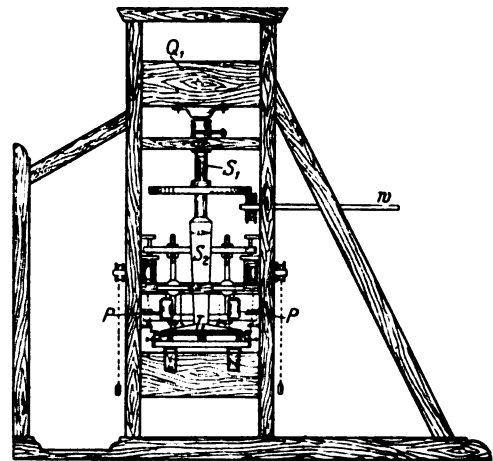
Koenigs erste Suhler Maschine (1803), Seitenansicht
